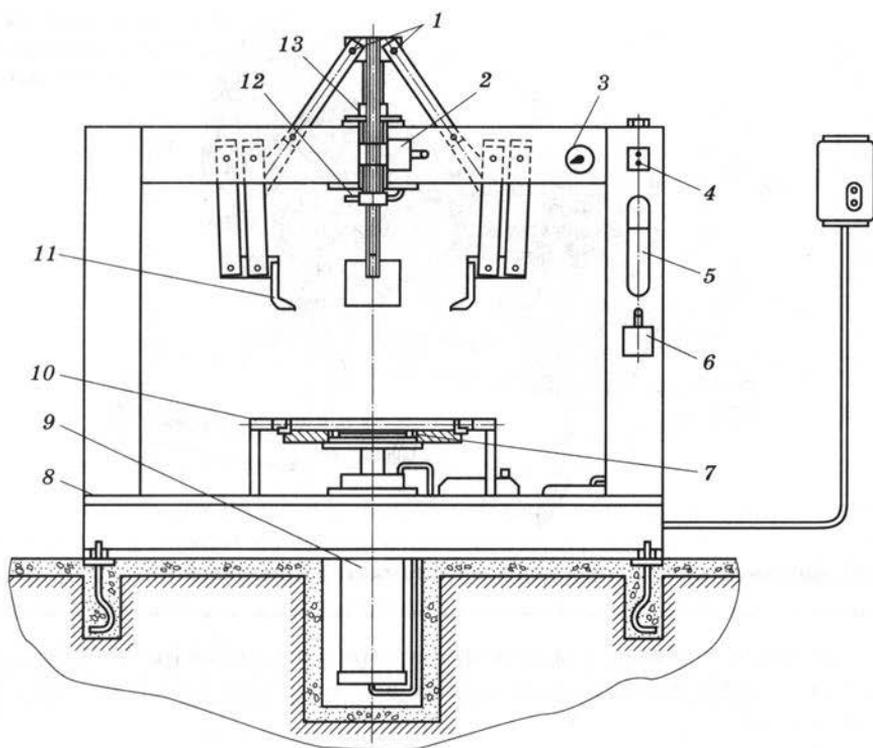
Стенд для демонтажа и монтажа шин грузовых автомобилей с вертикальным расположением колеса:
